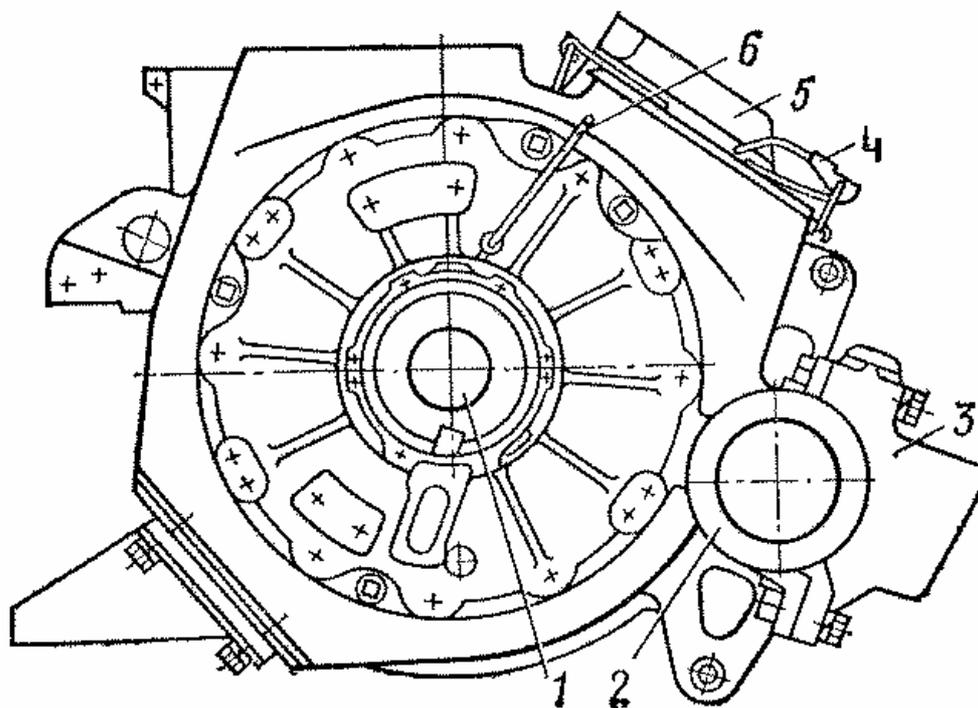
Общий вид тягового двигателя НБ-418К6
